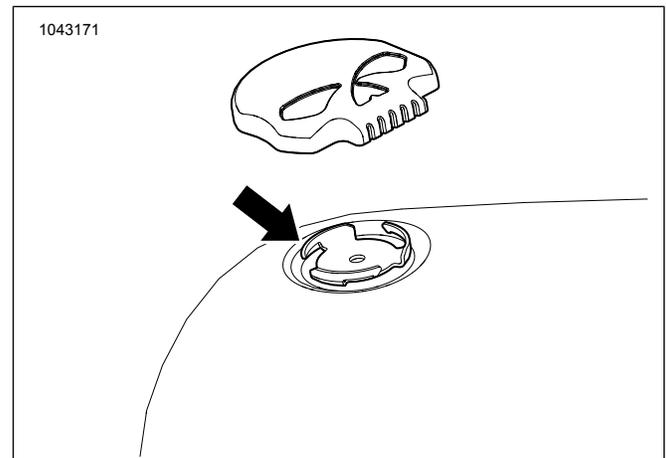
Lengüetas de alineación de la tapa izquierda del tanque de combustible
